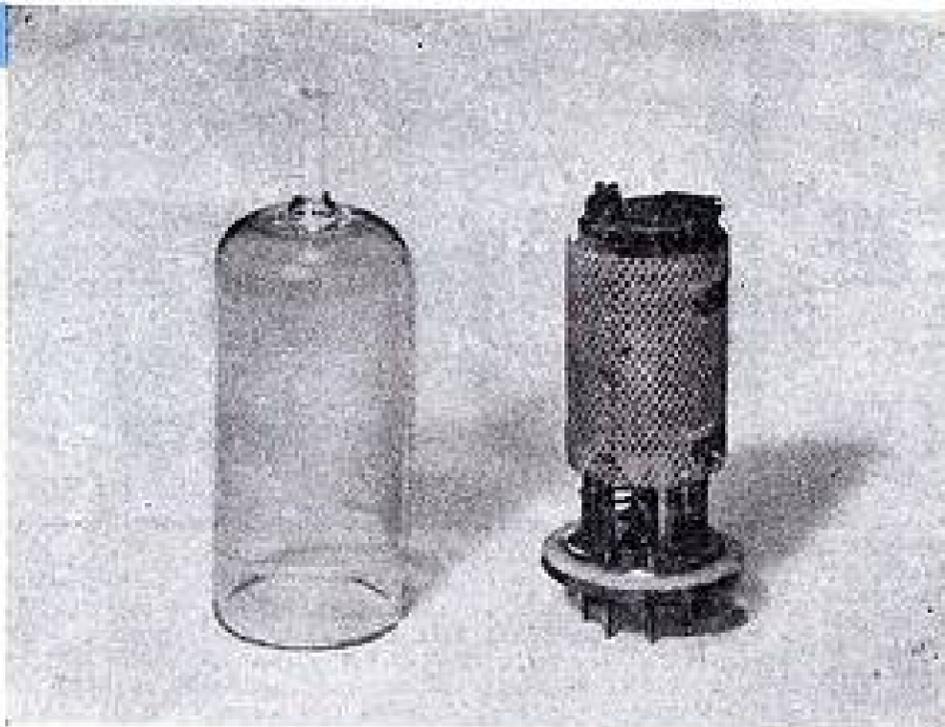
Tube « Rimlock » Philips-Miniwatt en cours de montage. On remarquera, sur la plaque de base, l'anneau d'émail destiné à sceller l'ampoule.
